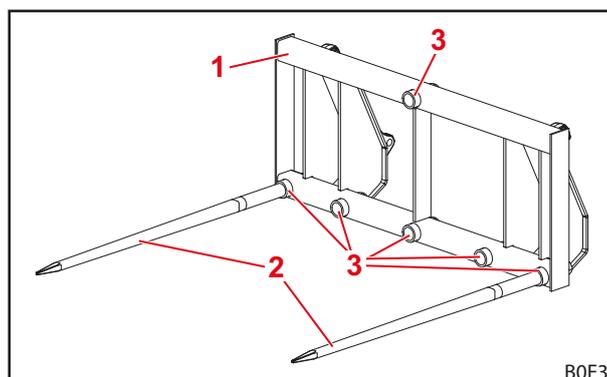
Estrutura da forquilha para fardos – Vista dianteira
